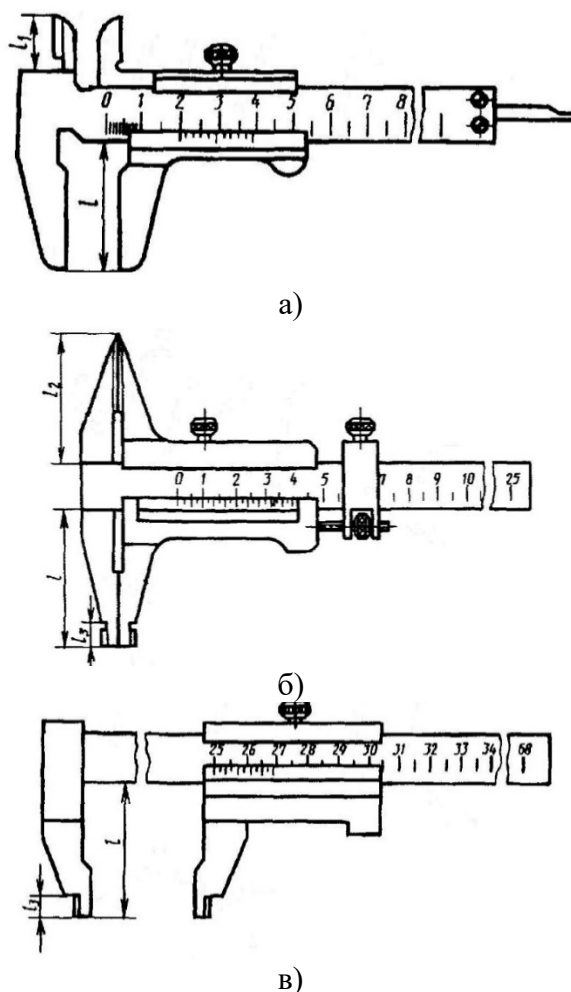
Схемы обозначения губок штангенциркулей модификаций:
